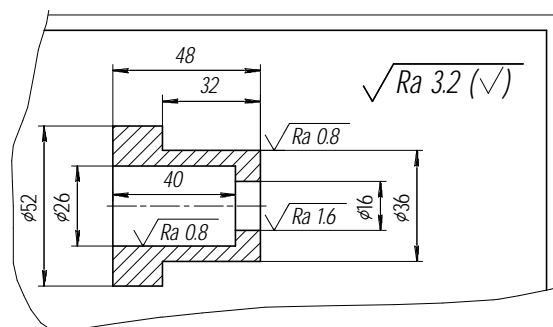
Чертеж детали с различной шероховатостью поверхности
